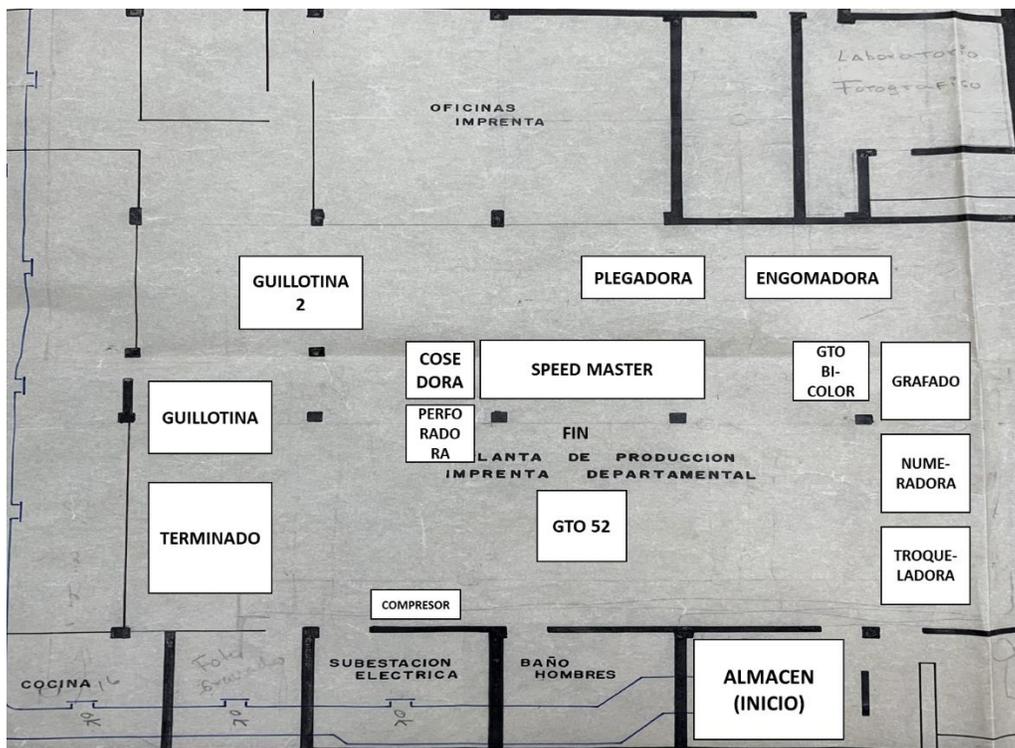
Plano de la planta IMPRETICS E.I.C.E.
